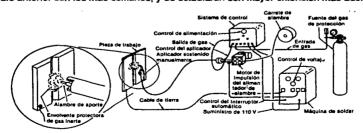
Partes componentes de un conjunto típico para soldadura GMAW o MIG
